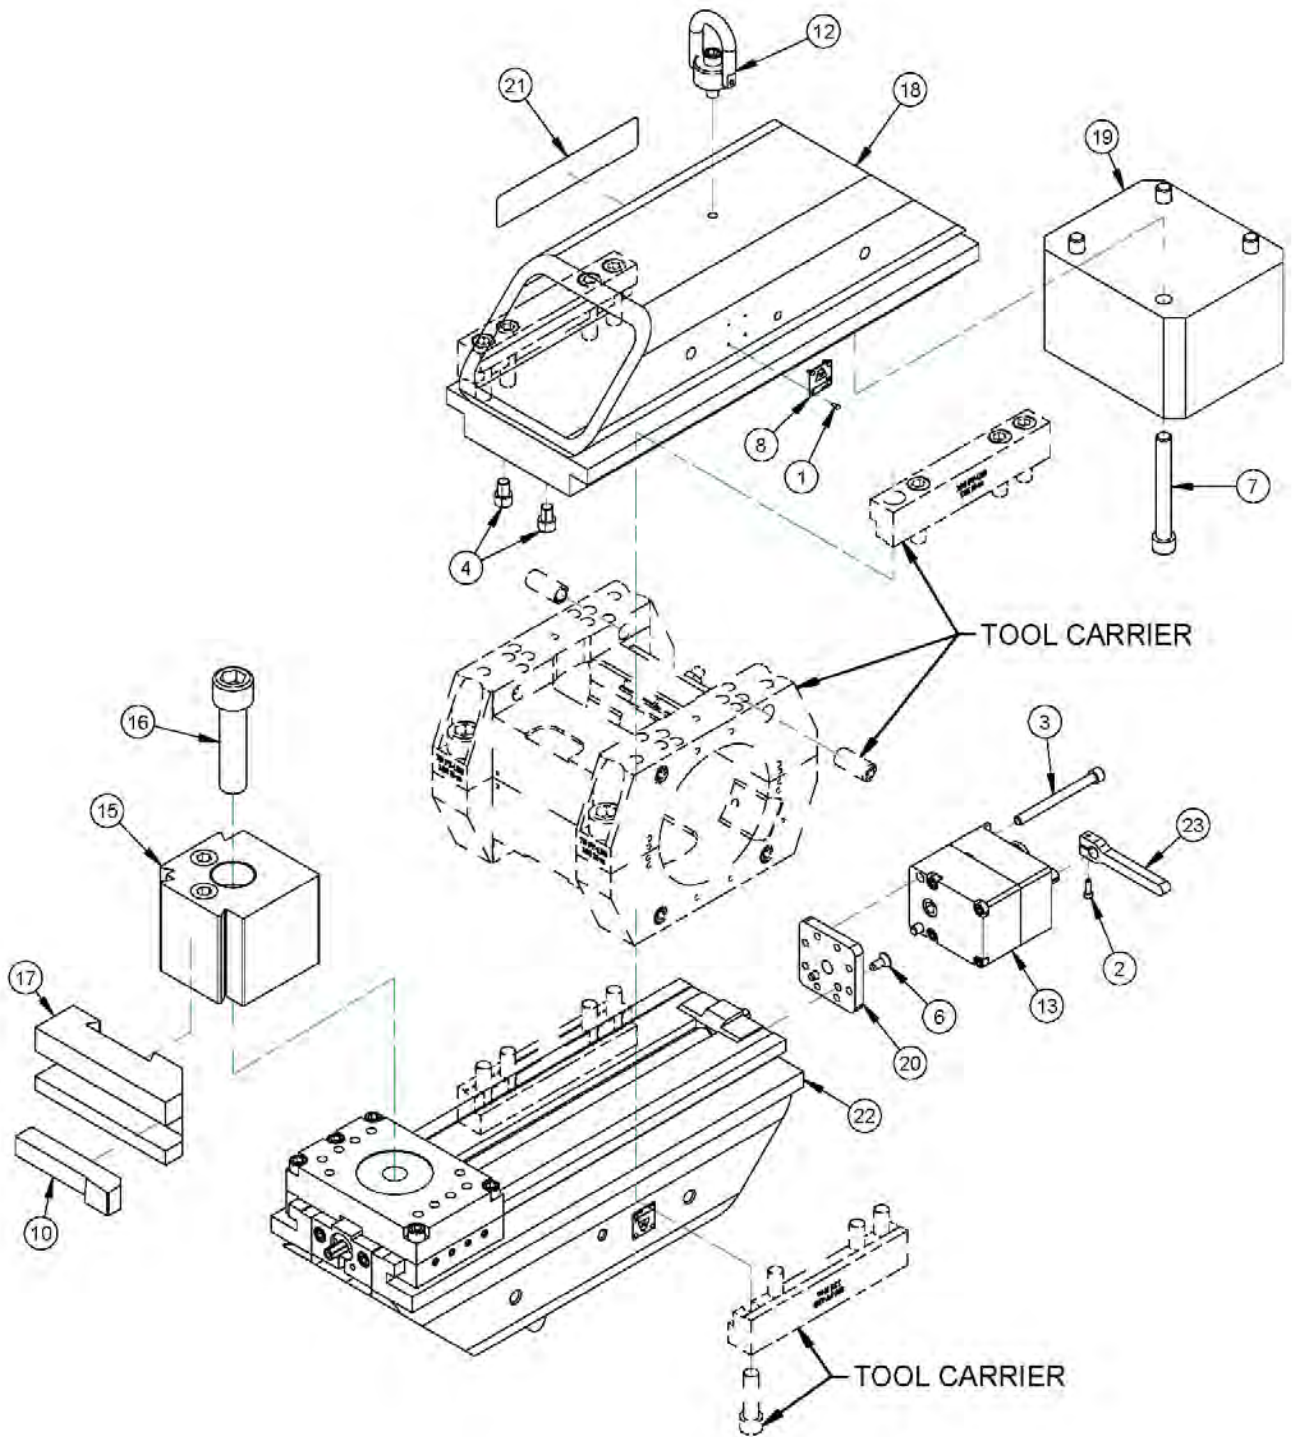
Подрезная головка в сборе (кат. № 75682)
